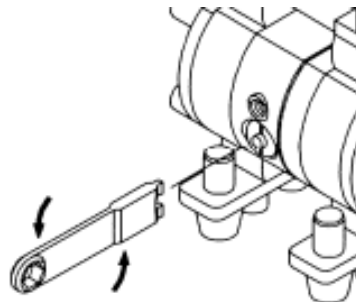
Desmontaje de válvula de carreta y conjunto de manguito 1
